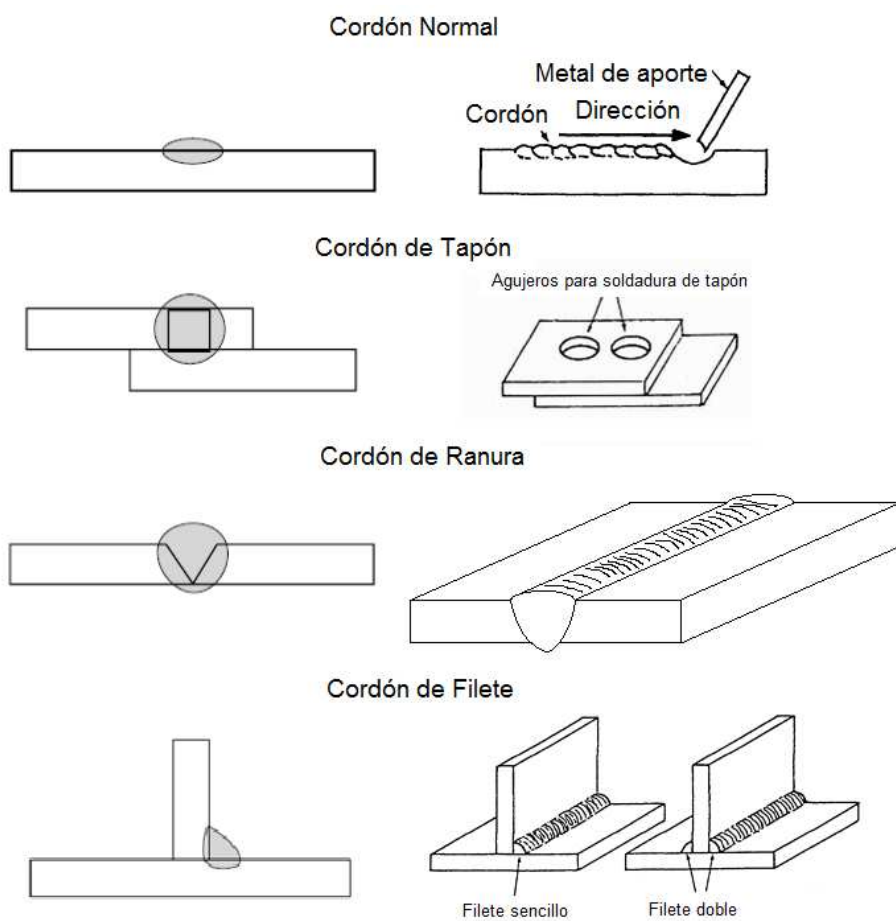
Tipos de cordones de soldadura<sup>2y4</sup>
